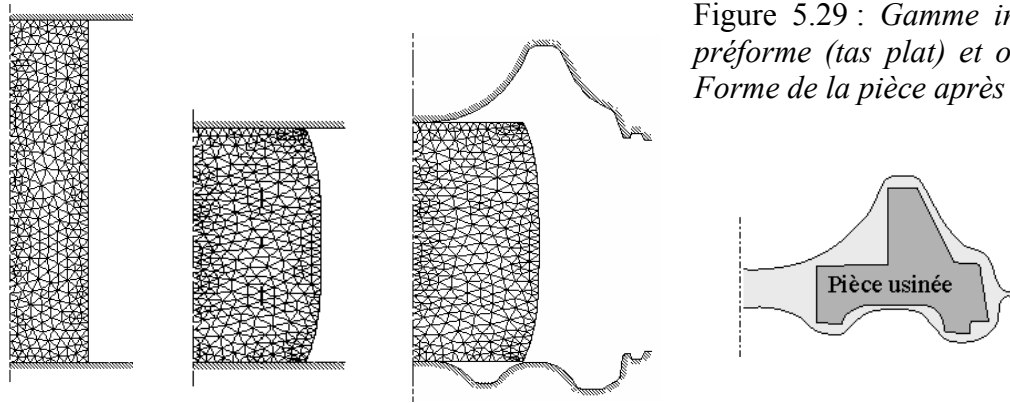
Gamme initiale, outil de préforme (tas plat) et outil de finition. Forme de la pièce après usinage.
